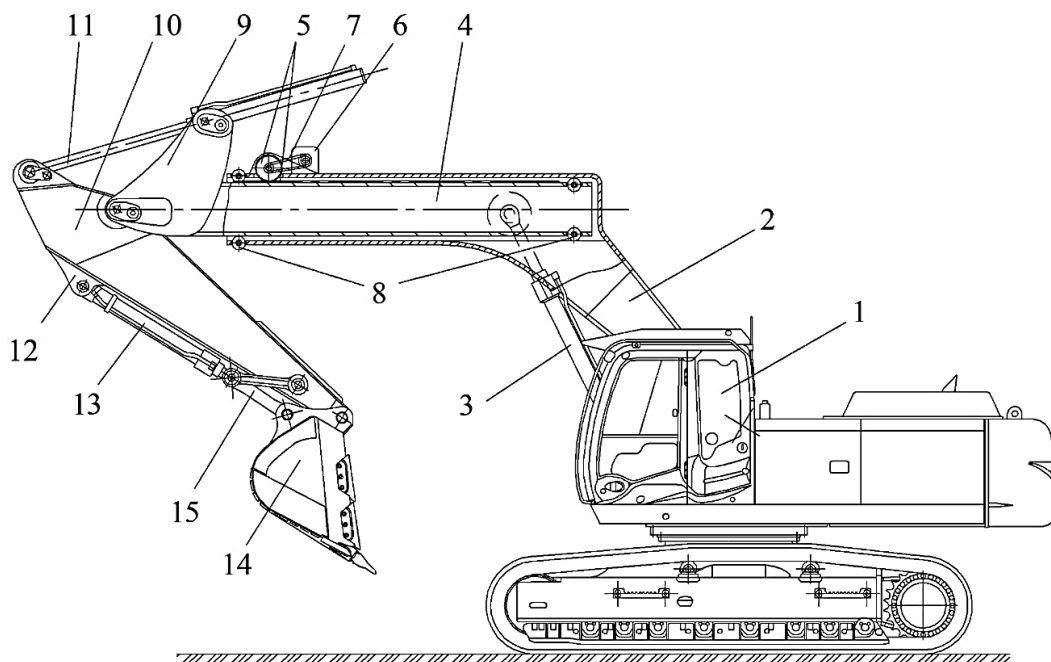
Конструктивна пропозиція патент на корисну модель №75318: 1 – базовий трактор; 2 – телескопічна стріла; 3, 11, 13 – гідроциліндри; 4 – ТС стріли; 5 – зубчасто-рейковий механізм; 6 – гідромотор; 7 – клинопасова передача; 8 – роликові опорні елементи; 9 – кронштейн; 10 – рукояті; 11 – гідроциліндр; 12 – кронштейн; 14 – ківш; 15 – чотириланковий механізм
